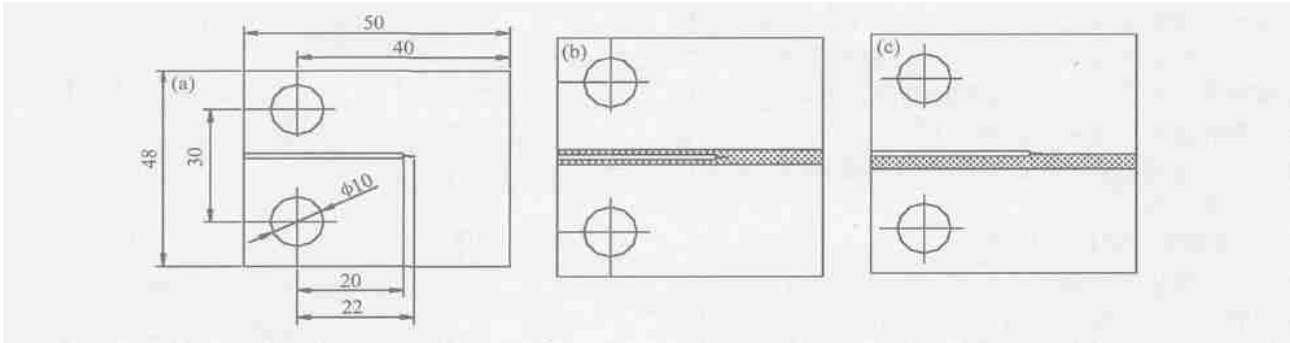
断裂韧性实验试样 (mm) (a) 母材试样; (b) 焊缝试样; (c) 热影响区试样
